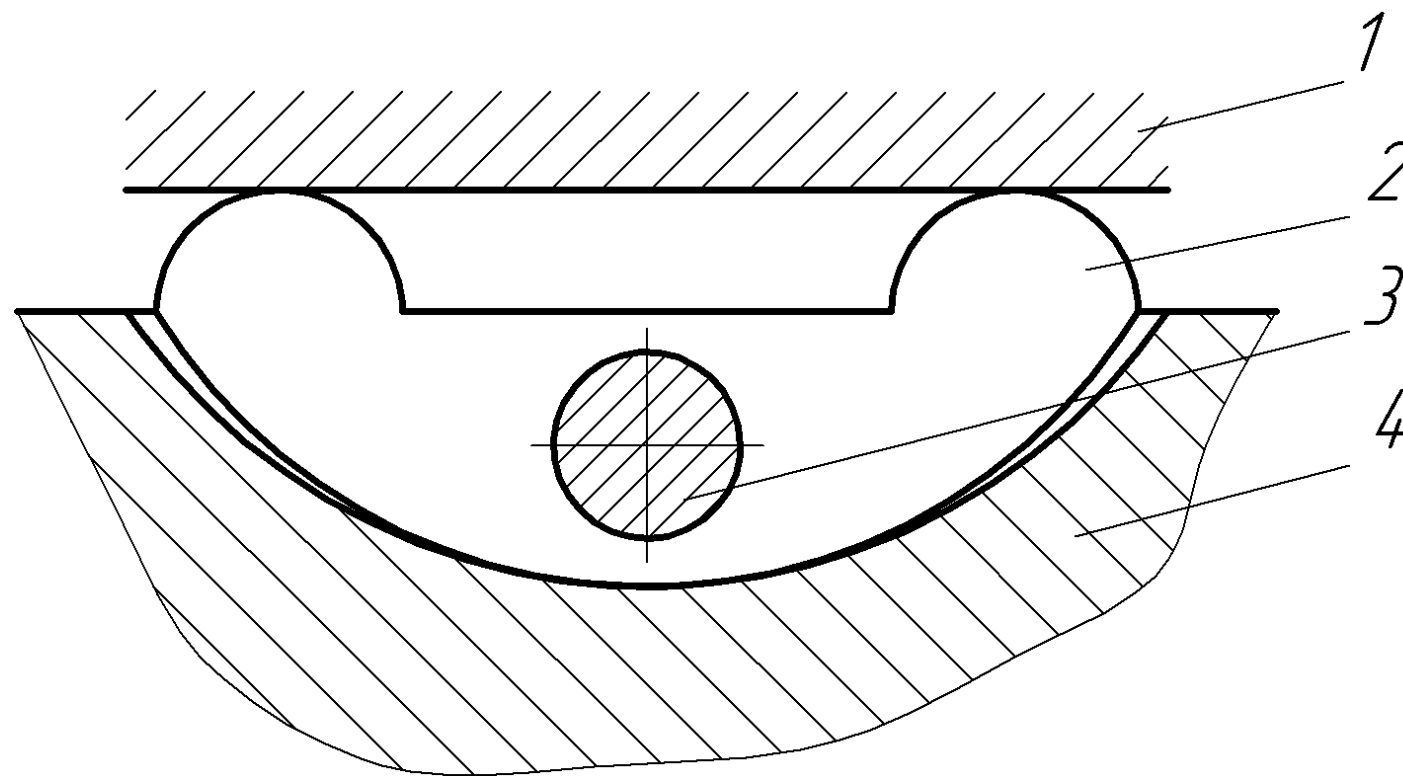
Конструкция самоустанавливающейся основной опоры:
